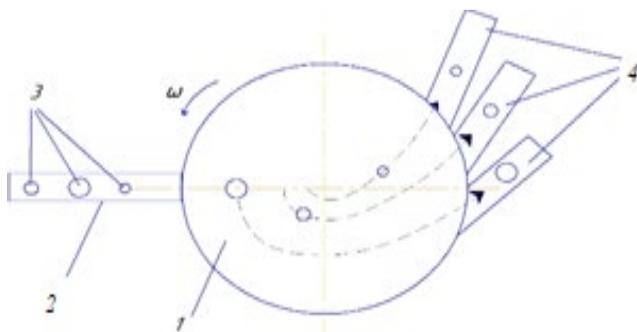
Устройство для активной ориентации и сортировки по размеру (вид сверху): 1 - диск; 2 - устройство поштучной загрузки; 3 - изделия; 4 - приемные лотки (улавливатели)
